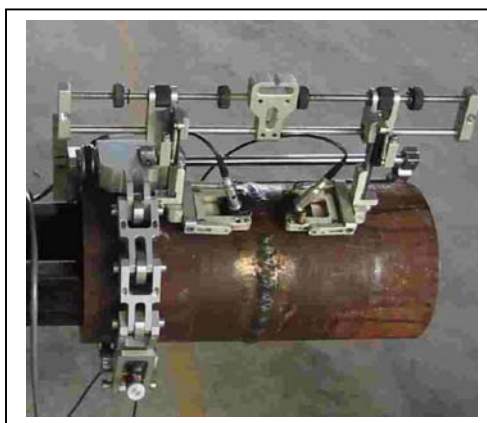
Contrôle TOFD d'une soudure de tuyauterie
